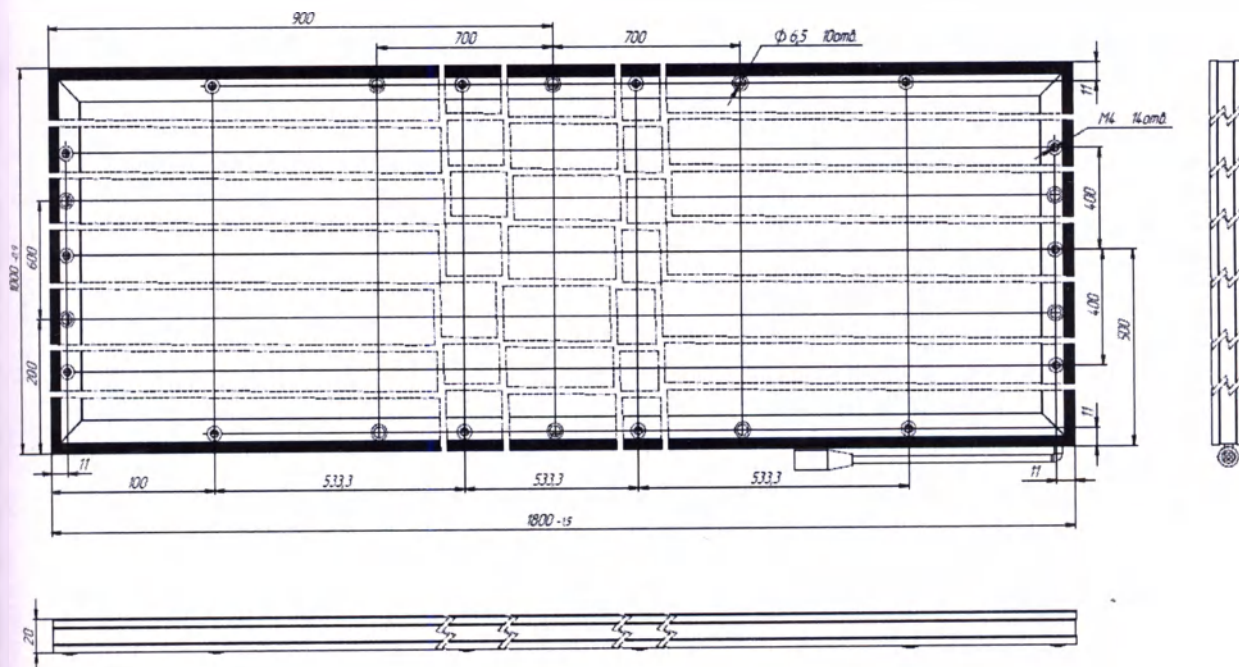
а – Габаритные и присоединительные размеры сегмента подсветки Lam-1/ Lam-4
